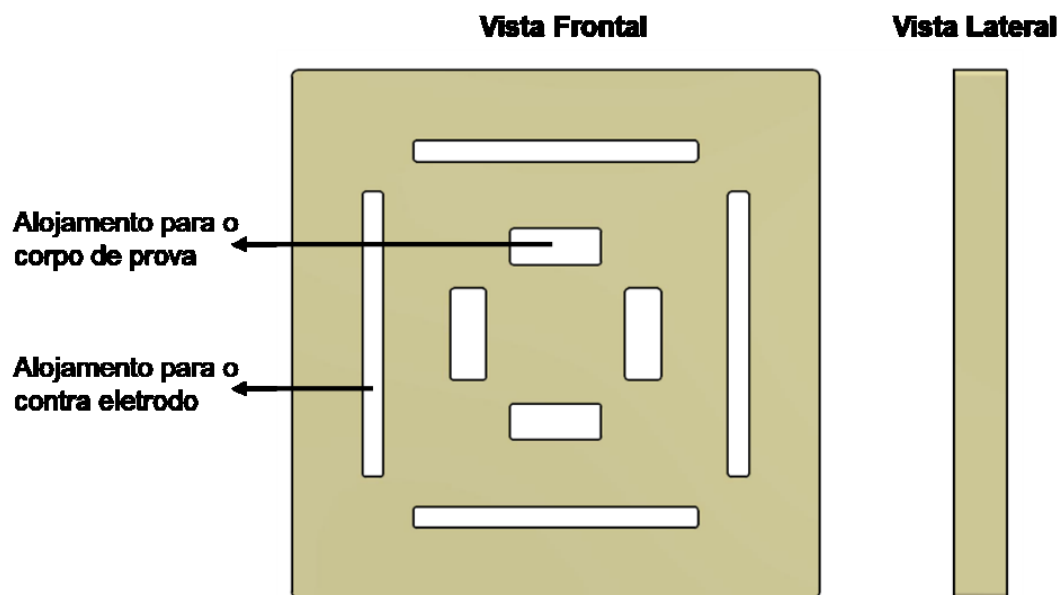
Desenho esquemático do suporte para a fixação dos corpos de prova.
